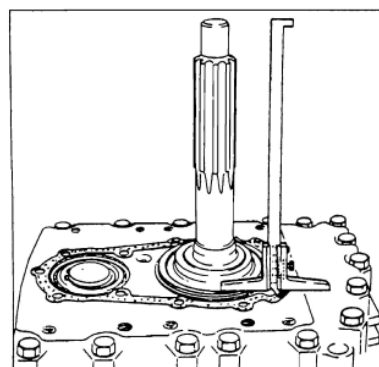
Вимірювання величини виступання роликотідшипника первинного вала.
